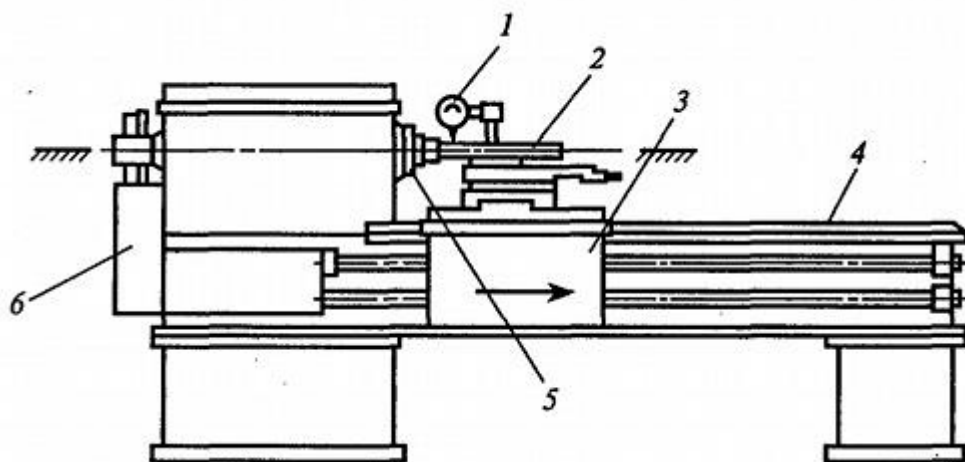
Схема проверки параллельности оси шпинделя направляющим станины: 1 — индикатор; 2 — цилиндрическая оправка; 3 — суппорт; 4 — направляющие станины; 5 — шпиндель; 6 — передняя бабка
